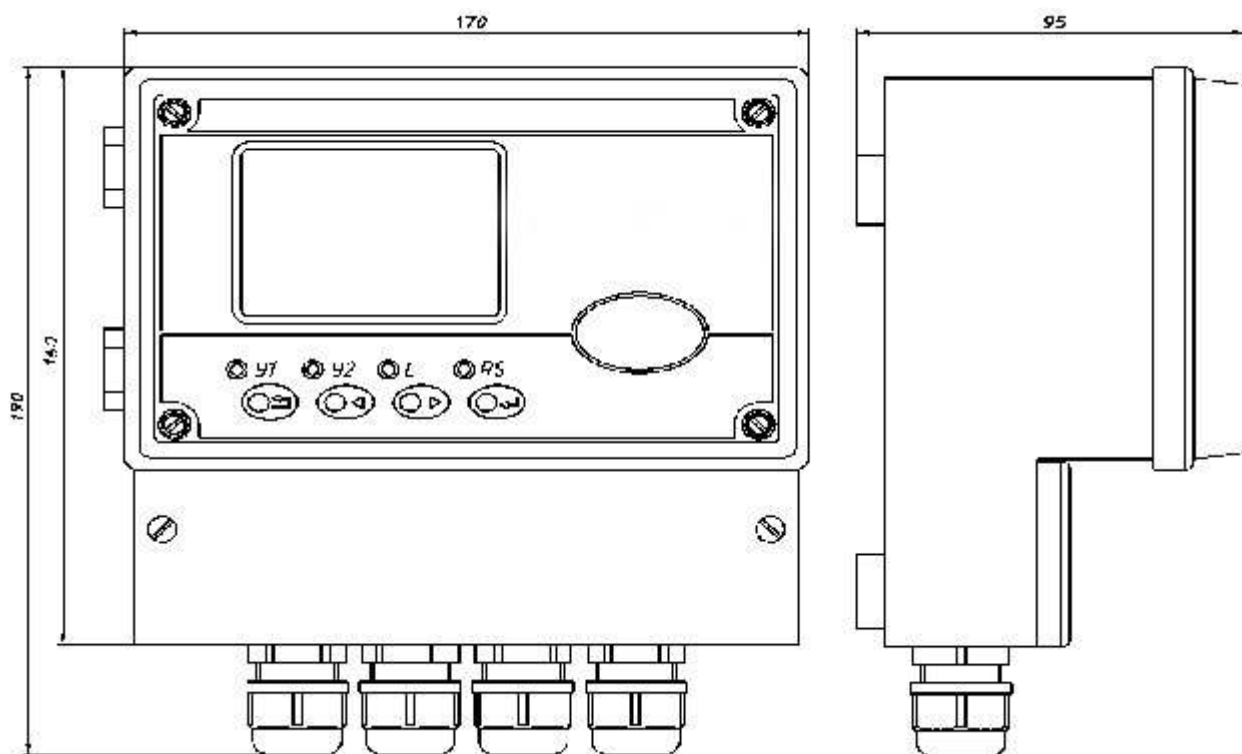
Габаритные и монтажные размеры измерительного прибора pH-4131
